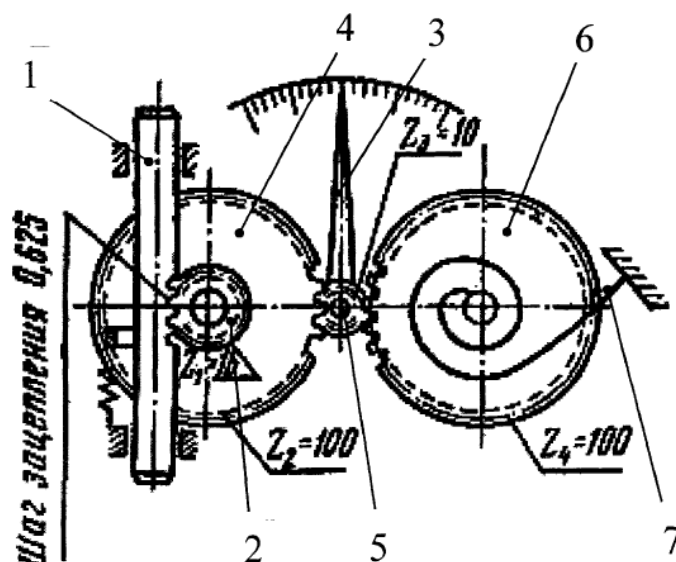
Кинематическая схема индикатора: 1 – измерительный стержень; 2,4,5,6 – зубчатые колеса; 3 – основная (большая) стрелка; 7 – спиральная пружина
